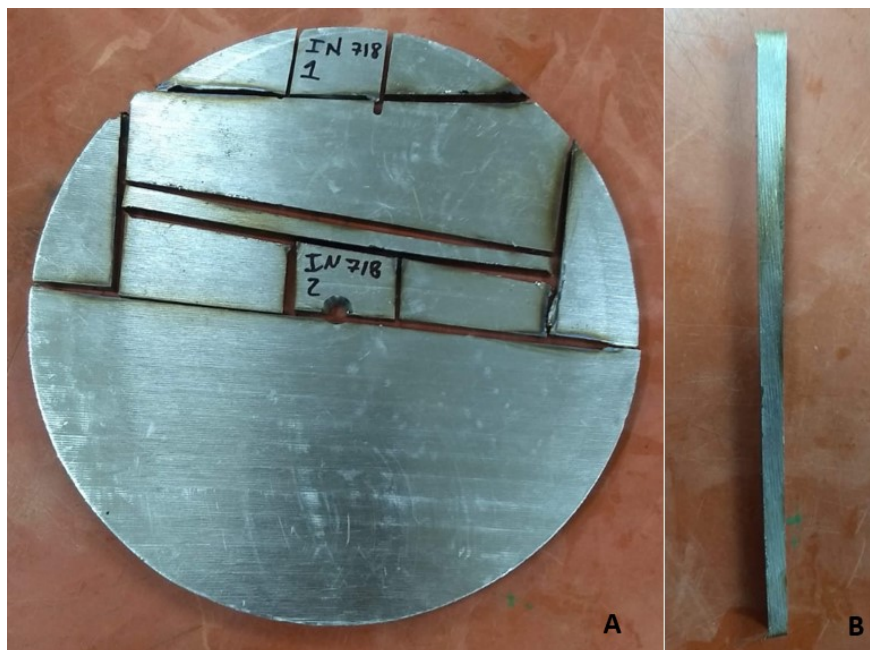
Corte transversal à barra de Inconel 718 e seus recortes (A). Haste de Inconel 718 utilizada no sistema termopar ferramenta-peça para compensação física (B).
